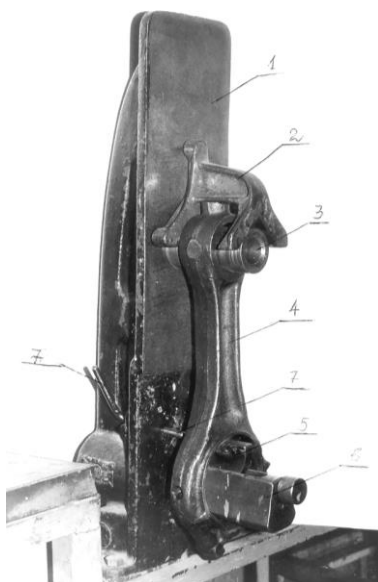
Приспособление для проверки шатуна на изгиб и скрученность:
